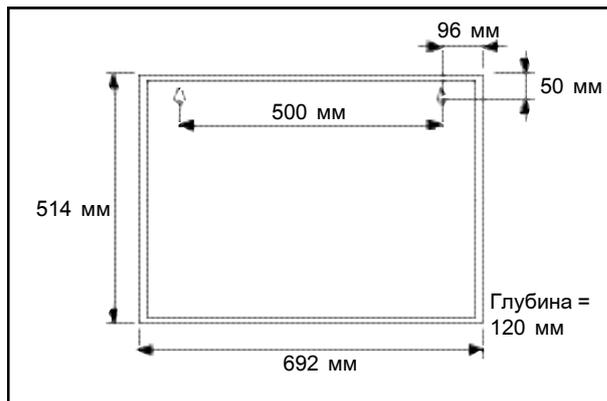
Установочные размеры корпуса зарядного устройства
